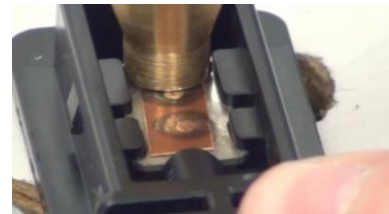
Exemple xapa de coure amb soldadura per punts TIG.
